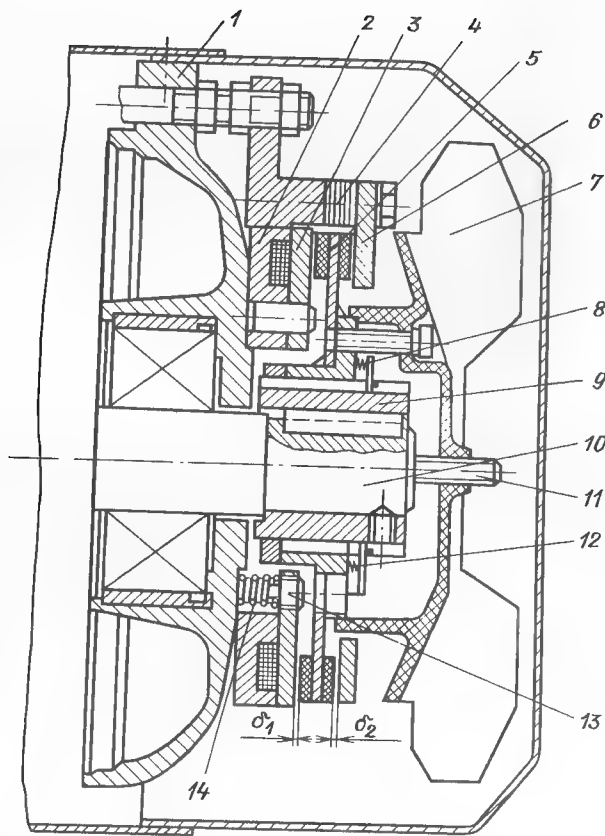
Пристроенный электромагнитный тормоз для АД серии АИ
